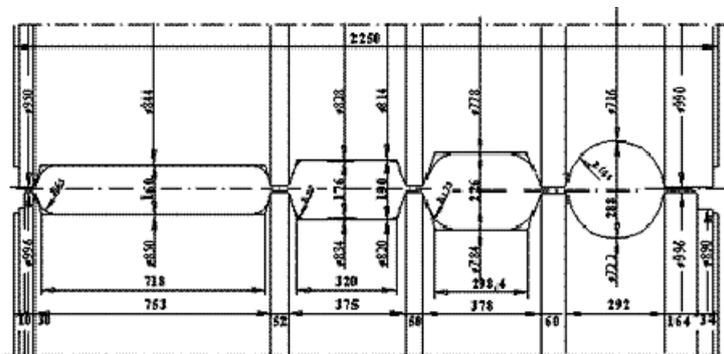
Калибровка валков блюминга 950 для прокатки круга 285мм
